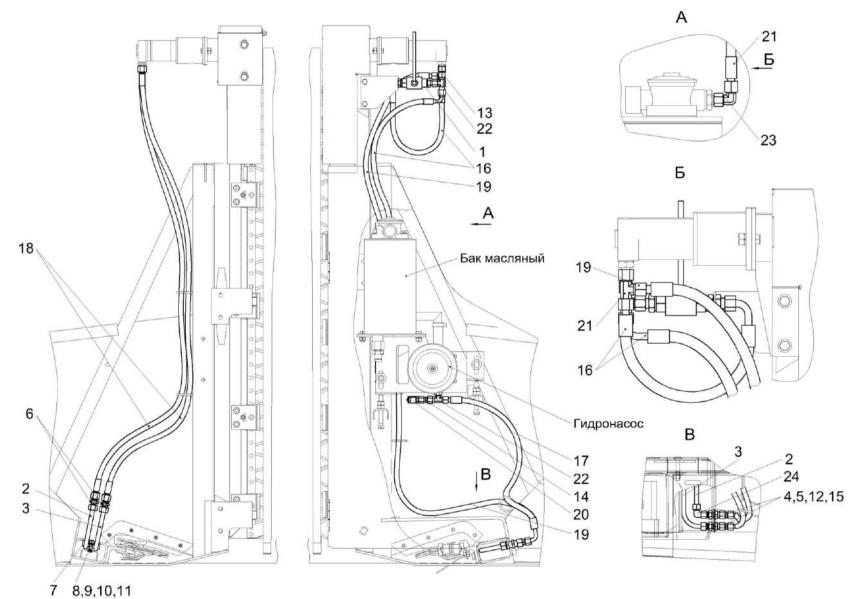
Гидросистема привода приспособления для уборки рапса КЗК-9-1542000
